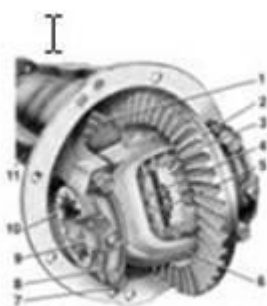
Редуктор заднего моста: 1 — ведущая шестерня; 2 — ведомая шестерня; 3 — сателлит; 4 — шестерня полуоси; 5 — ось сателлитов; 6 — коробка дифференциала; 7 — болты крепления крышки подшипника коробки дифференциала; 8 — крышка подшипника коробки дифференциала; 9 — пластина стопорная; 10 — регулировочная гайка
